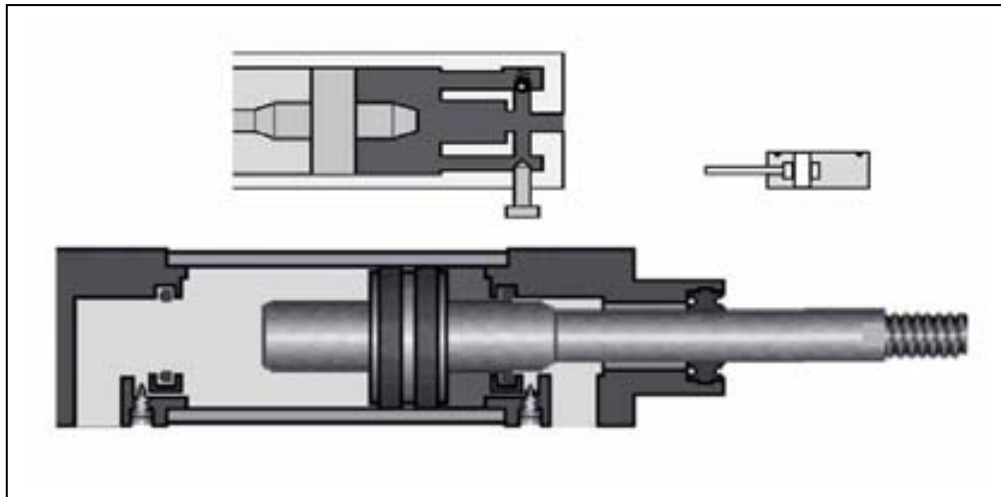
Amortiguamiento de final de carrera del pistón. Fuente: Norgren
